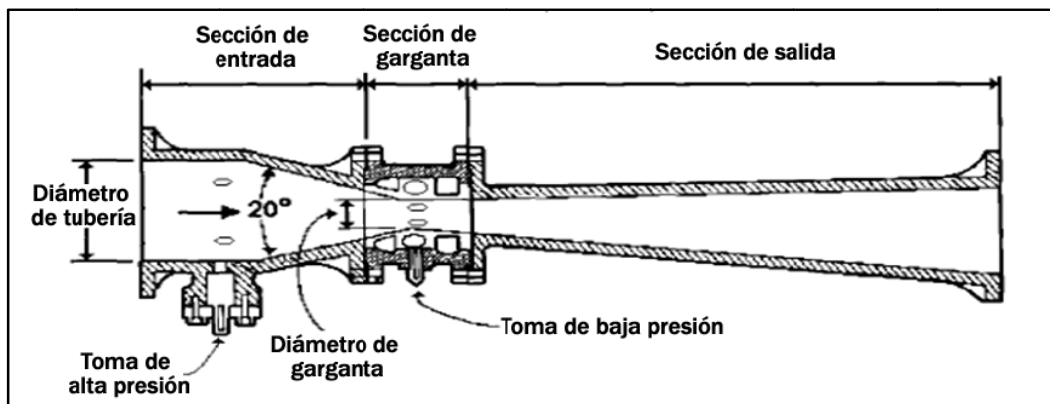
Partes principales que integran un tubo de Venturi.
